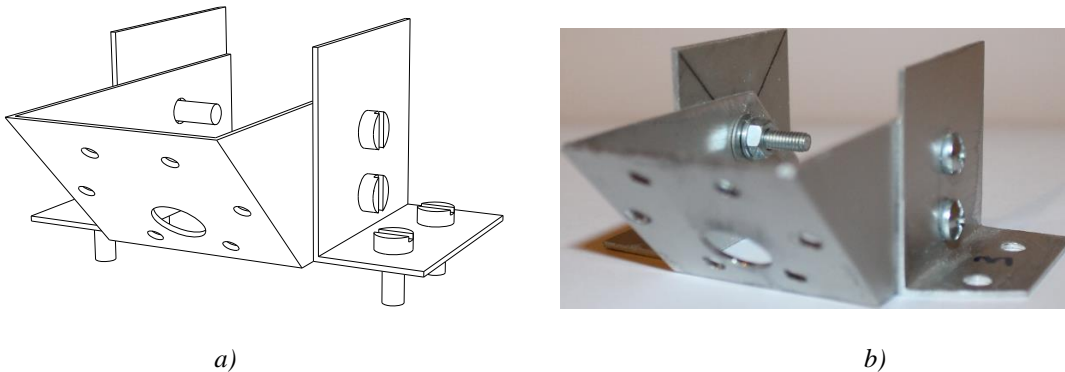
Soporte de motores. a) diseño CAD b) construcción física.
